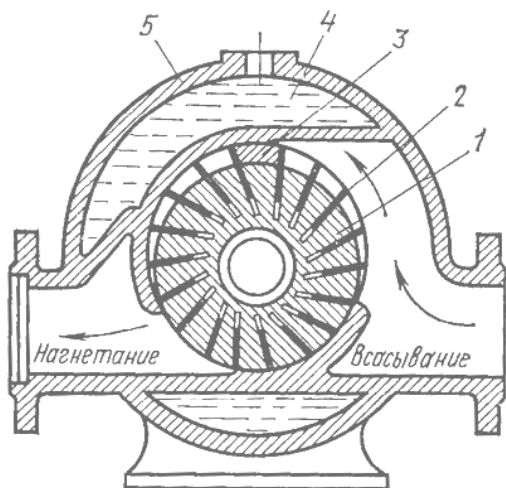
Роторно-пластинчатый компрессор с вращающимся ротором:
